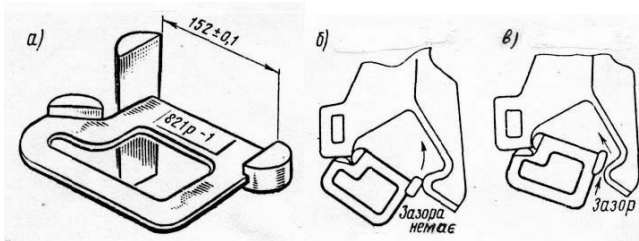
Шаблон 821р-1 для перевірки ширини зіву корпусу автозчепу:
